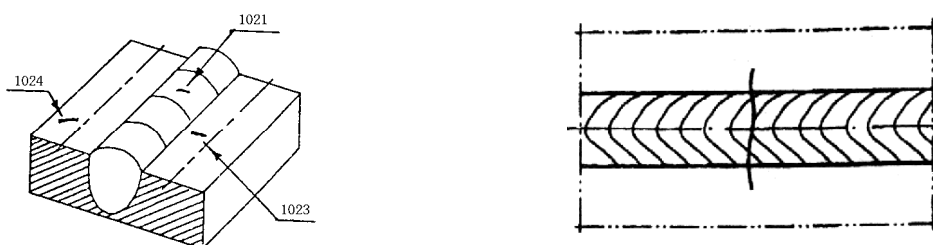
Поперечная трещина сварного соединения
